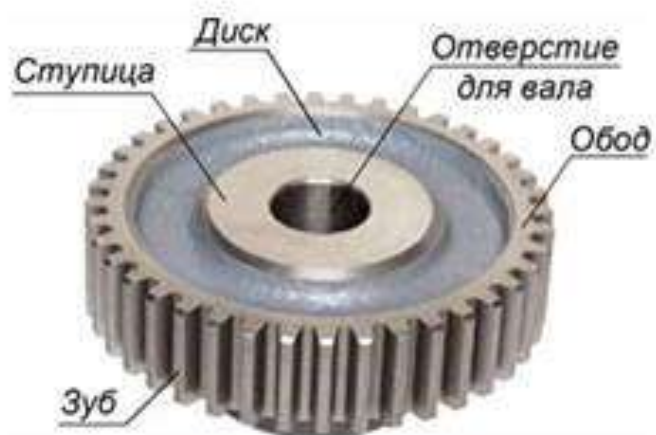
Конструкция зубчатого колеса (внешний вид)
